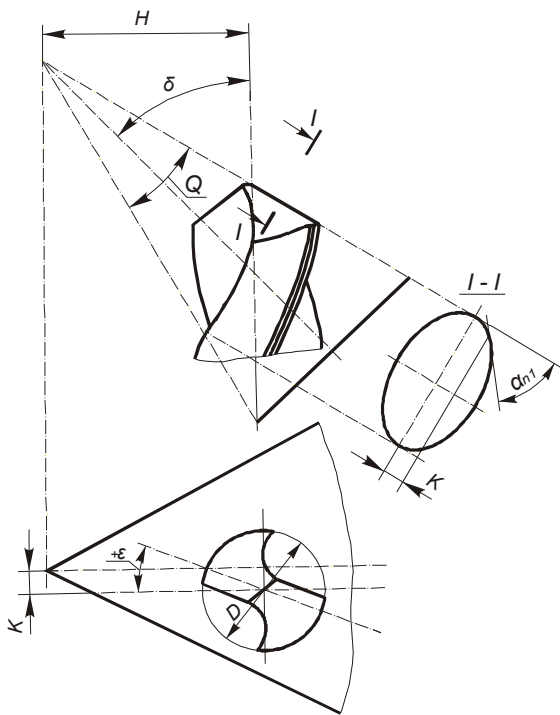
Формування конічної задньої поверхні свердла
